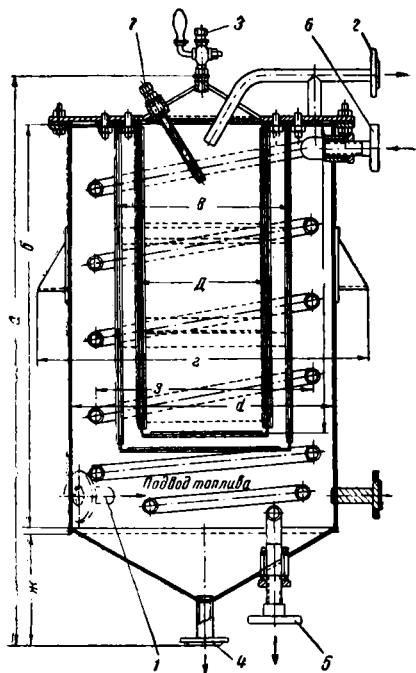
Конструкция отстойника для топлива: 1 — подвод топлива; 2 — выход топлива; 3 — вход пара; 4 — выход конденсата; 5 — аварийный спуск; 6 — спуск отстоя; 7 — вытяжная труба
